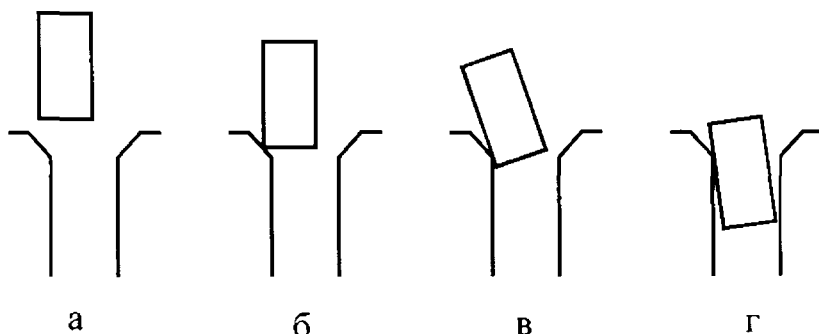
Схема запресування циліндричного стержня: а – підведення стержня; б – торкання зенківки; в – однокотковий контакт стержня; г – двоточковий контакт.
